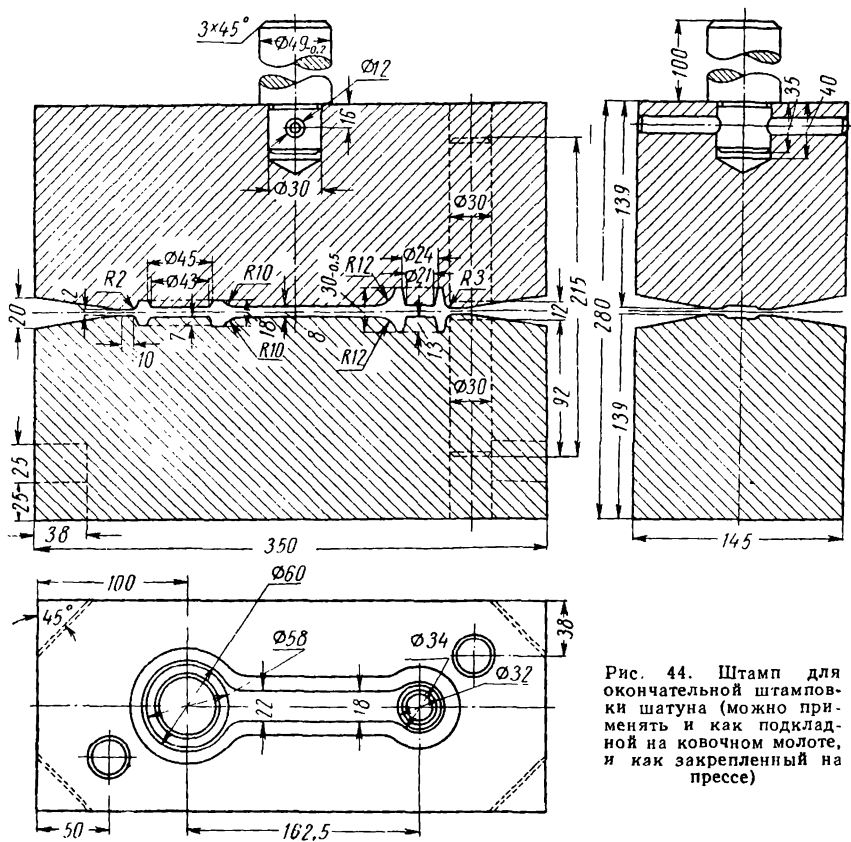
Штамп для окончательной штамповки шатуна (можно применять и как подкладной на ковочном молоте, и как закрепленный на прессе)
